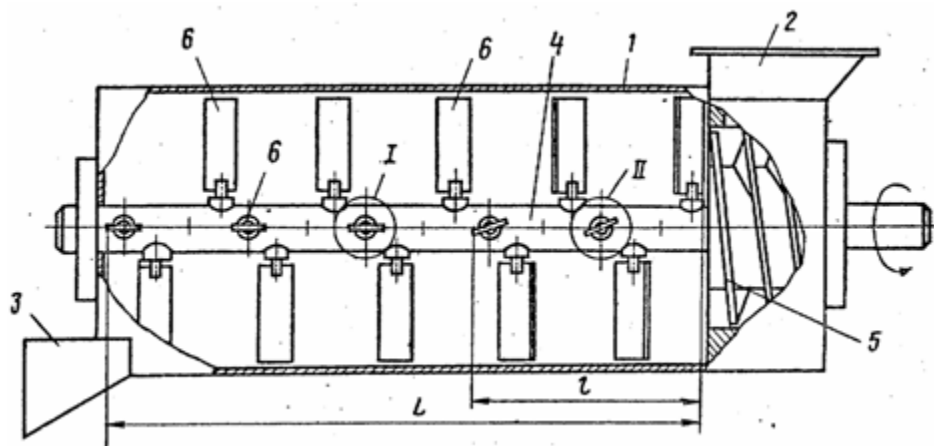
Змішувач-гранулятор: 1 - корпус; 2,3 - патрубки завантаження і вивантаження; 4- вал; 5- шнек; 6- лопатки.
